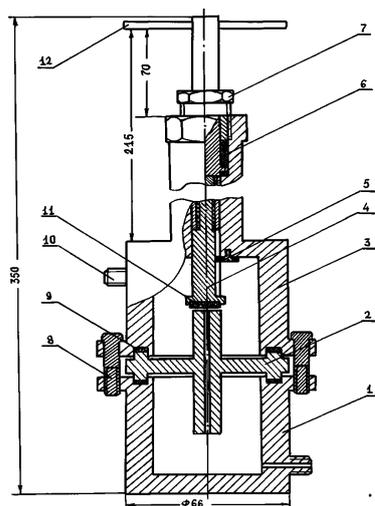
Двухколбовый диффузионный аппарат. 1 - корпус нижней колбы; 2 - блок капилляров; 3 - корпус верхней колбы; 4 - шток; 5 - фиксатор; 6 - фторопластовые уплотнения; 7 - гайка; 8 - болт; 9 - фторопластовая прокладка; 10 - штуцер для подключения к газовой магистрали; 11 - фторопластовая таблетка; 12 - вороток.
